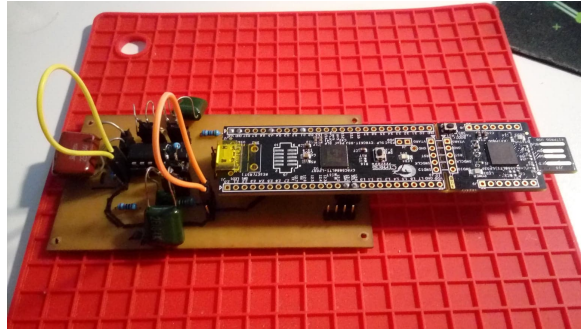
Placa de circuito impresso - Componentes Removíveis.
